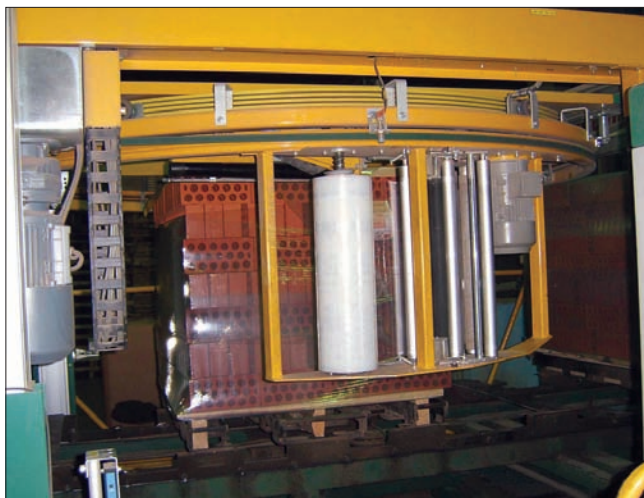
Общий вид установки для обмотки пакетов стретч-пленкой
